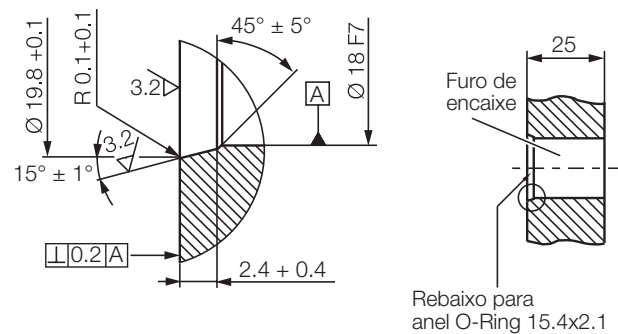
Furo de encaixe para montagem do BTL com anel O-ring
